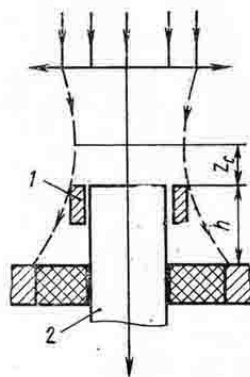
Схема сварки осесимметричных соединений:
